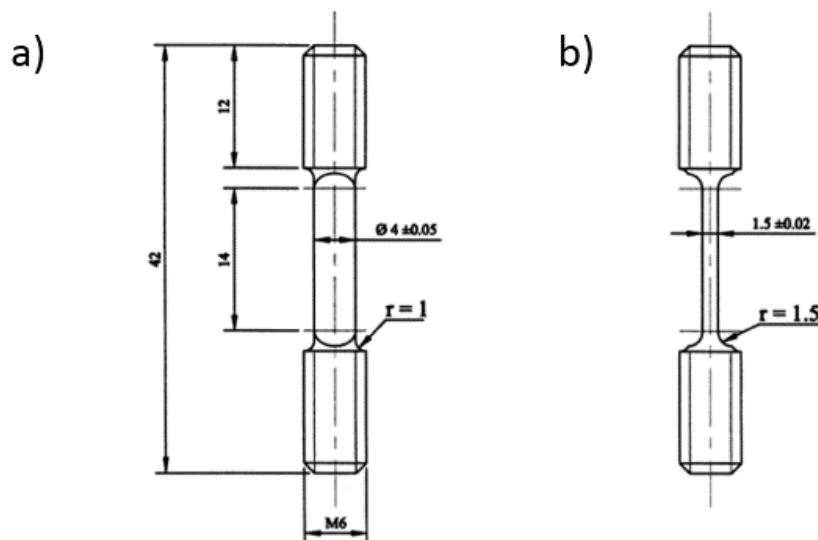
Géométries éprouvettes cylindriques avec méplats pour fortes charges - vue présentant un méplat a) de face et b) de profil
